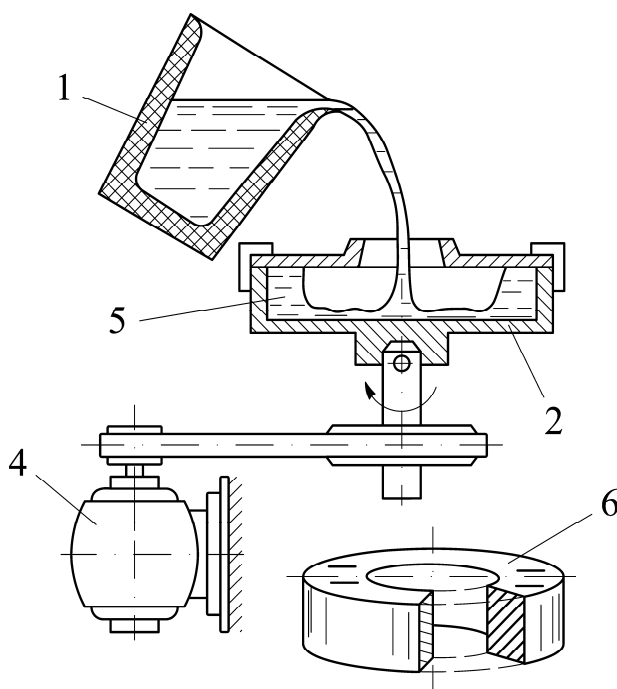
Схема получения отливки при вращении формы вокруг вертикальной оси: 1 – ковш; 2 – форма; 3 – шпиндель; 4 – электродвигатель; 5 – расплав; 6 – отливка
